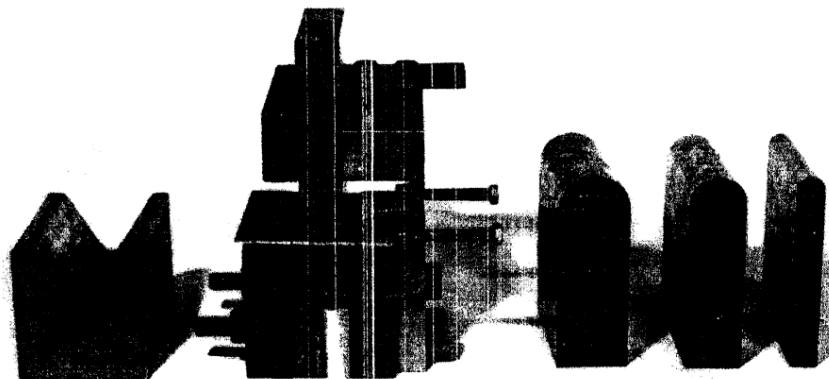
Универсальный гибочный штамп со сменными пуансонами и матрицами
